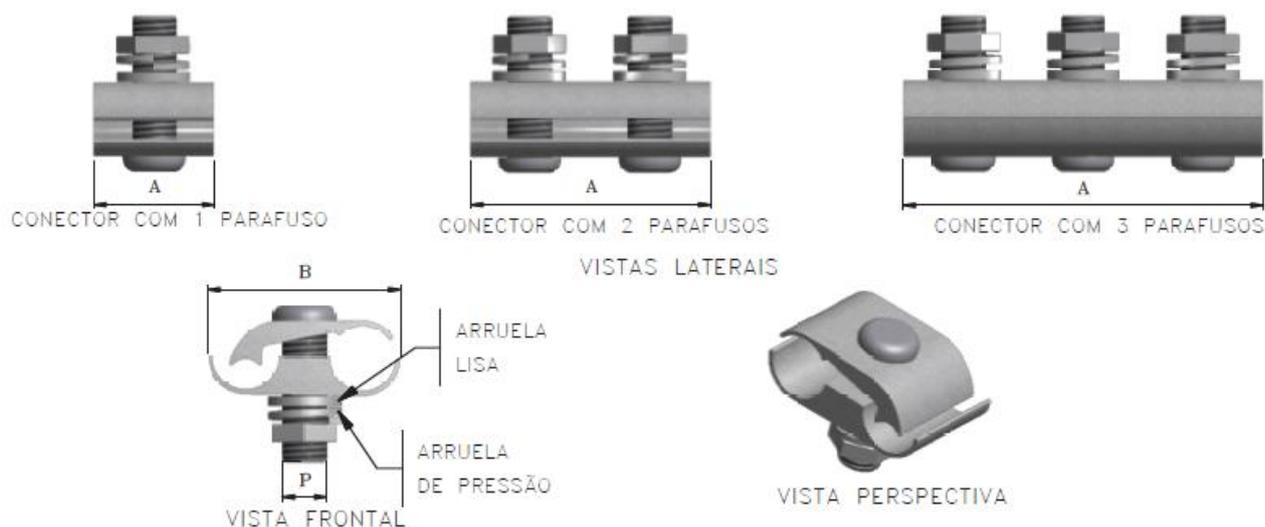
Vistas do Conector Paralelo para Conexões Bimetálicas
